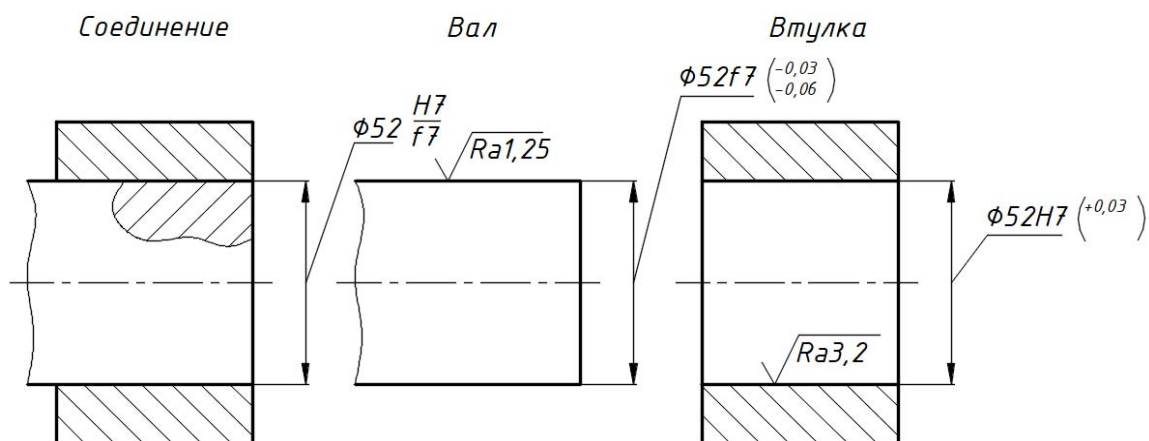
Эскизы соединения, вала и корпуса (втулки)
